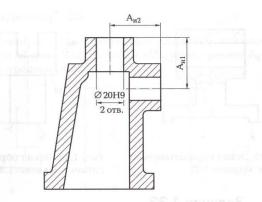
Эскиз обрабатываемой детали к заданию 1.30
